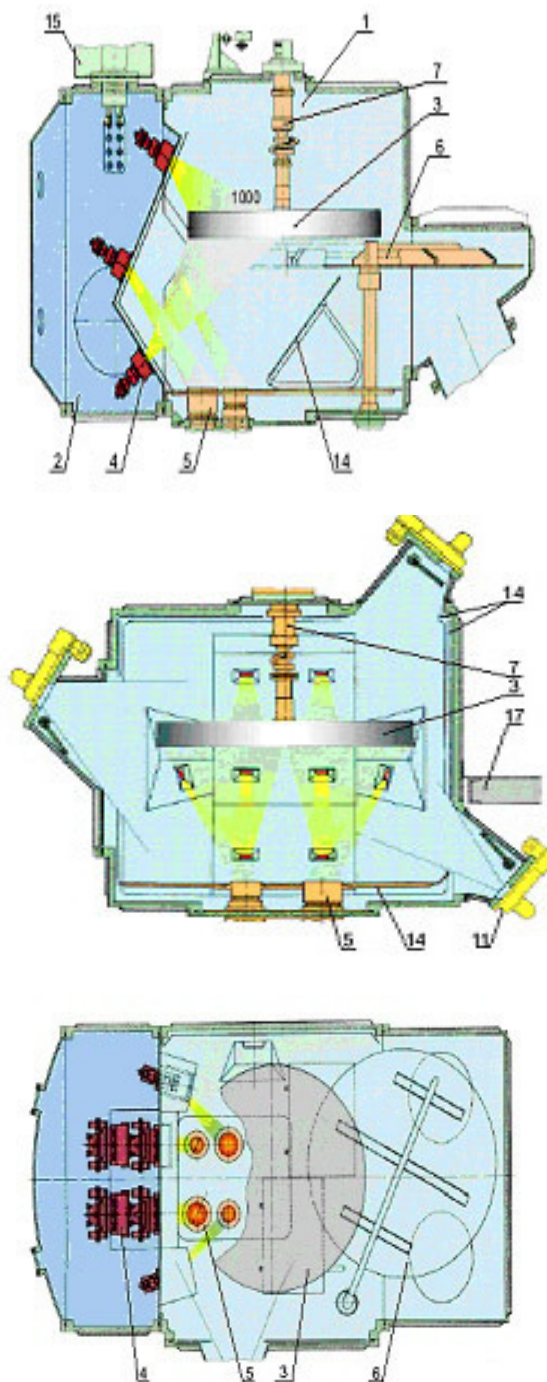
Схема промислової електронно-променевої установки Л-5 для виготовлення матеріалів і сплавів: 1 – робоча камера, 2 – камера гармат, 3 – виріб; 4 – електронні гармати, 5 – блок тиглів; 6 – заслінка, 7 – механізм підвіски і обертання виробу, 8 – механізми подачі зливків; 9 – вакуумна система; 10 – система охолодження; 11 – оглядова система; 12 – пульт управління, 13 – шафи управління; 14 – екрани; 15 – високовольне введення; 16 – маніпулятор, 17 – майданчик обслуговування
